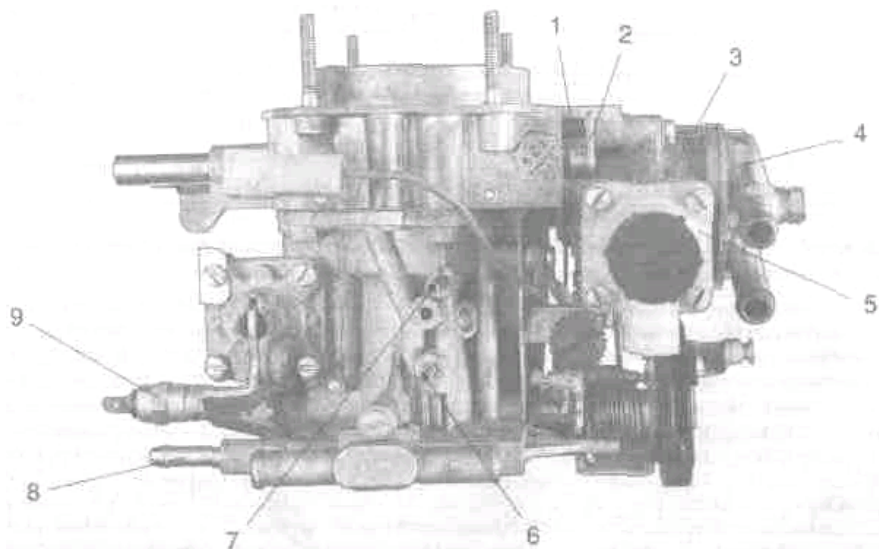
Вид на карбюратор 21083 -1107010 - 62 со стороны вакуумного диафрагменного механизма
